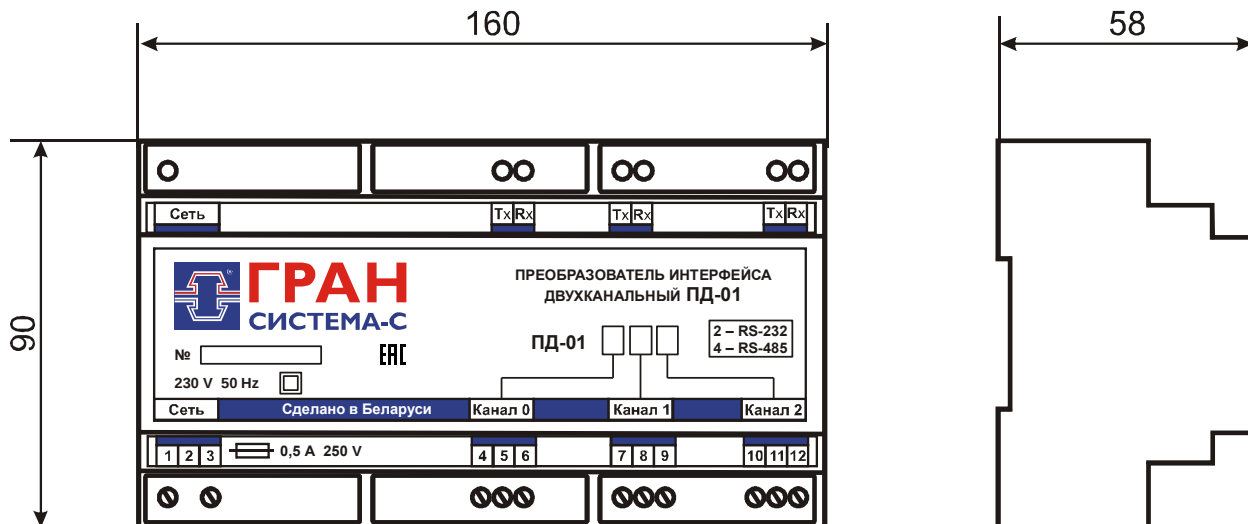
Габаритные размеры преобразователя ПД-01
